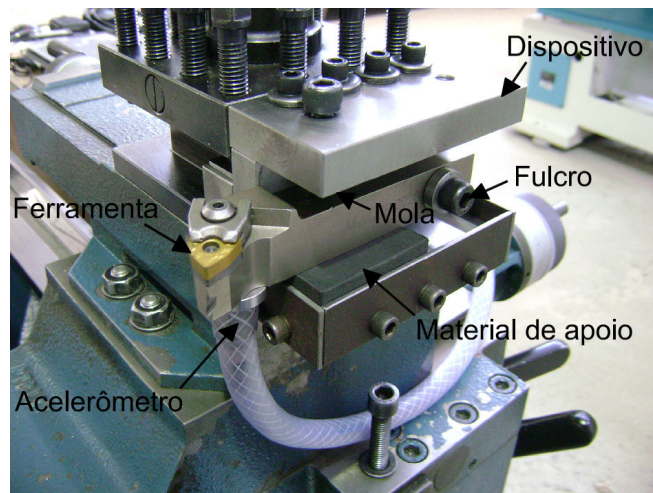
Dispositivo para usinagem dos corpos de prova.
